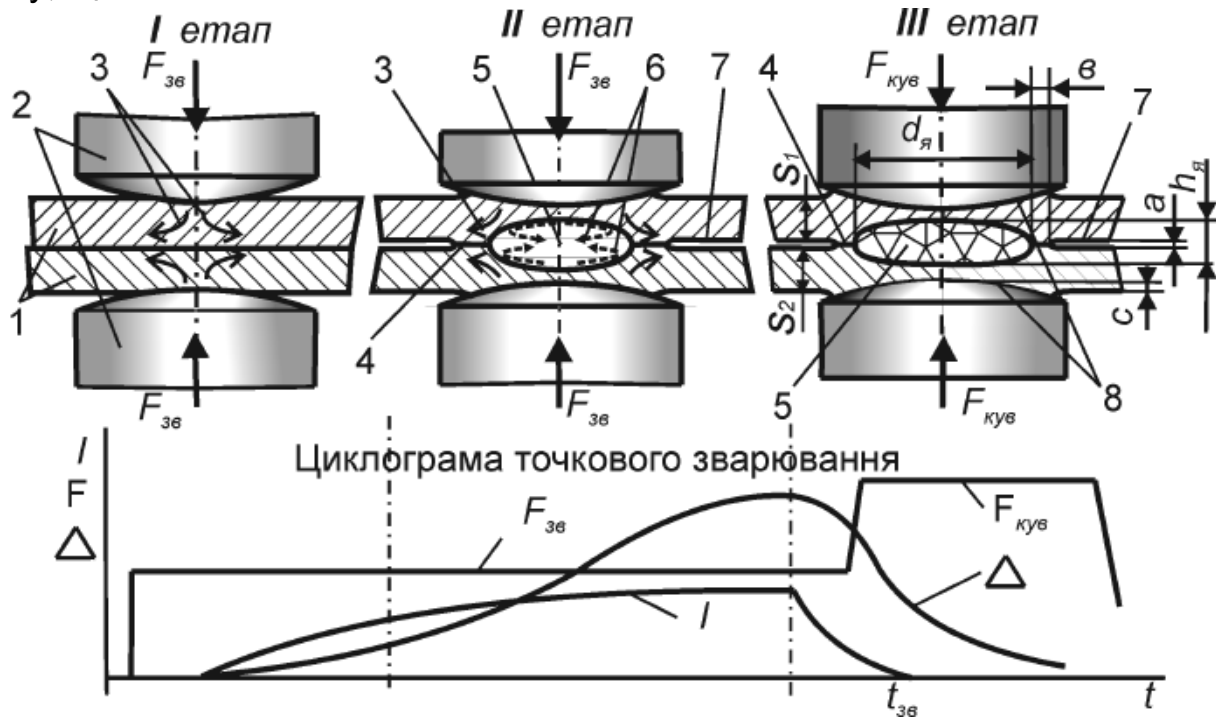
Етапи утворення з'єднання при точковому зварюванні: 1 – деталі, що зварюються; 2 – електроди; 3 – напрямок максимальної деформації; 4 – ущільнювальний пояс; 5 – лите ядро; 6 – напрямок перемішування металу ядра; 7 – зазор між листами; 8 – вм'ятини від електродів; 9 – точка, що закристалізувалася; $F_{зе}$ – зусилля стискання при зварюванні; $F_{кув}$ – зусилля проковування; S_1 , S_2 – товщина листів, що зварюються; $h_я$ – висота ядра; $d_я$ – діаметр ядра; a – величина розходження листів; $в$ – ширина ущільнювального паса; $с$ – глибина вм'ятини; I – зварювальний струм; Δ – переміщення електрода
